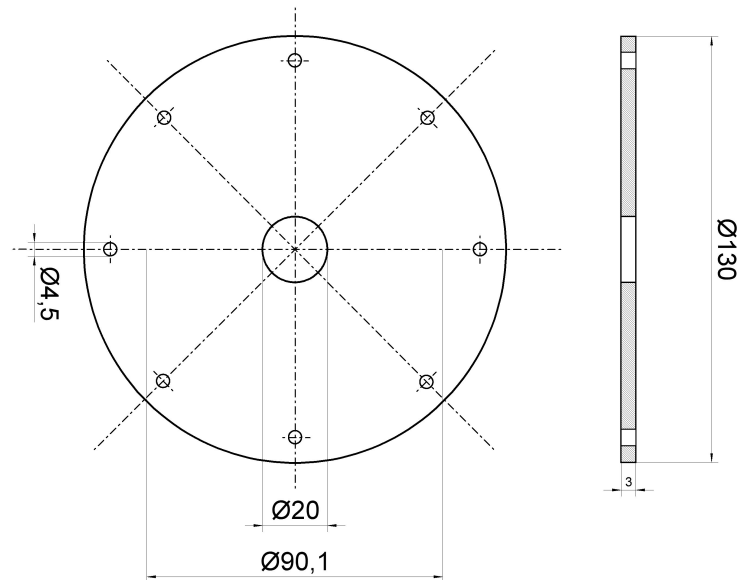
Technische Zeichnung der Kamerabefestigungsplatte
